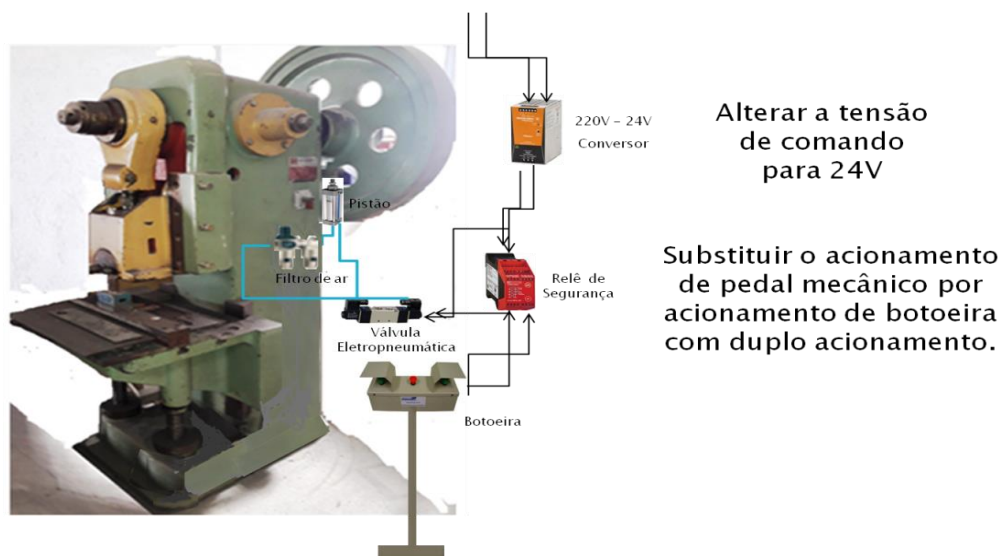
Adequação proposta 2 – Instalações de Dispositivos Elétricos
